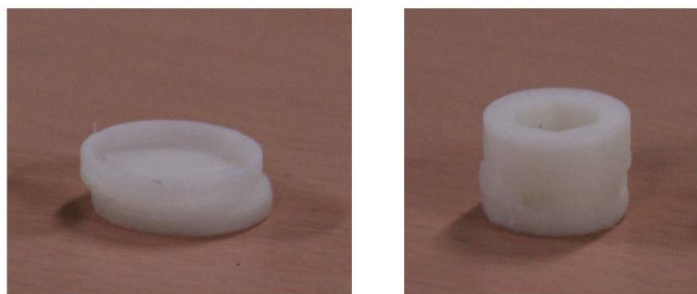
Piezas defectuosas: Cubierta superior (izquierda), cubierta tuerca (derecha).
